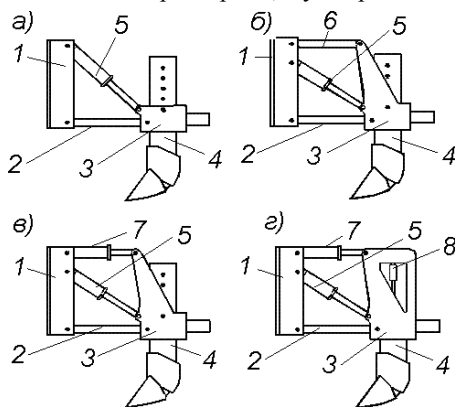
Типы рыхлительного оборудования: а) – трёхзвенное; б), в), г) – четырёхзвенное; 1 – опорная рама; 2 – нижняя тяговая рама; 3 – рабочая балка; 4 – рыхлящий зуб; 5 – гидроцилиндры подъёма и опускания рабочей балки; 6 – верхняя тяговая рама; 7 – гидроцилиндры наклона зуба; 8 – механизм изменения вылета зуба.
